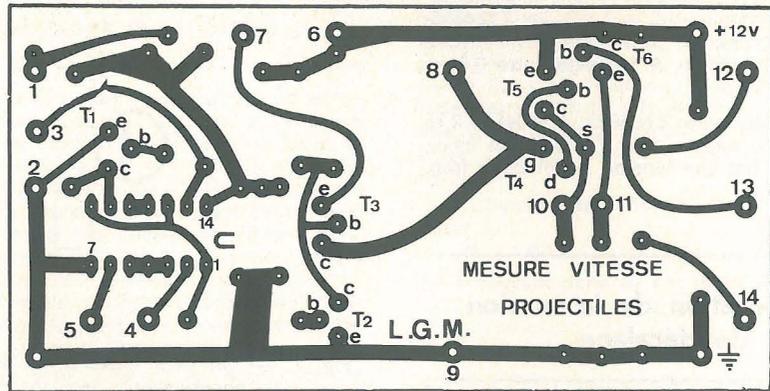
Dessin du circuit imprimé prévu pour recevoir le montage précédent, vu du côté du cuivre.
